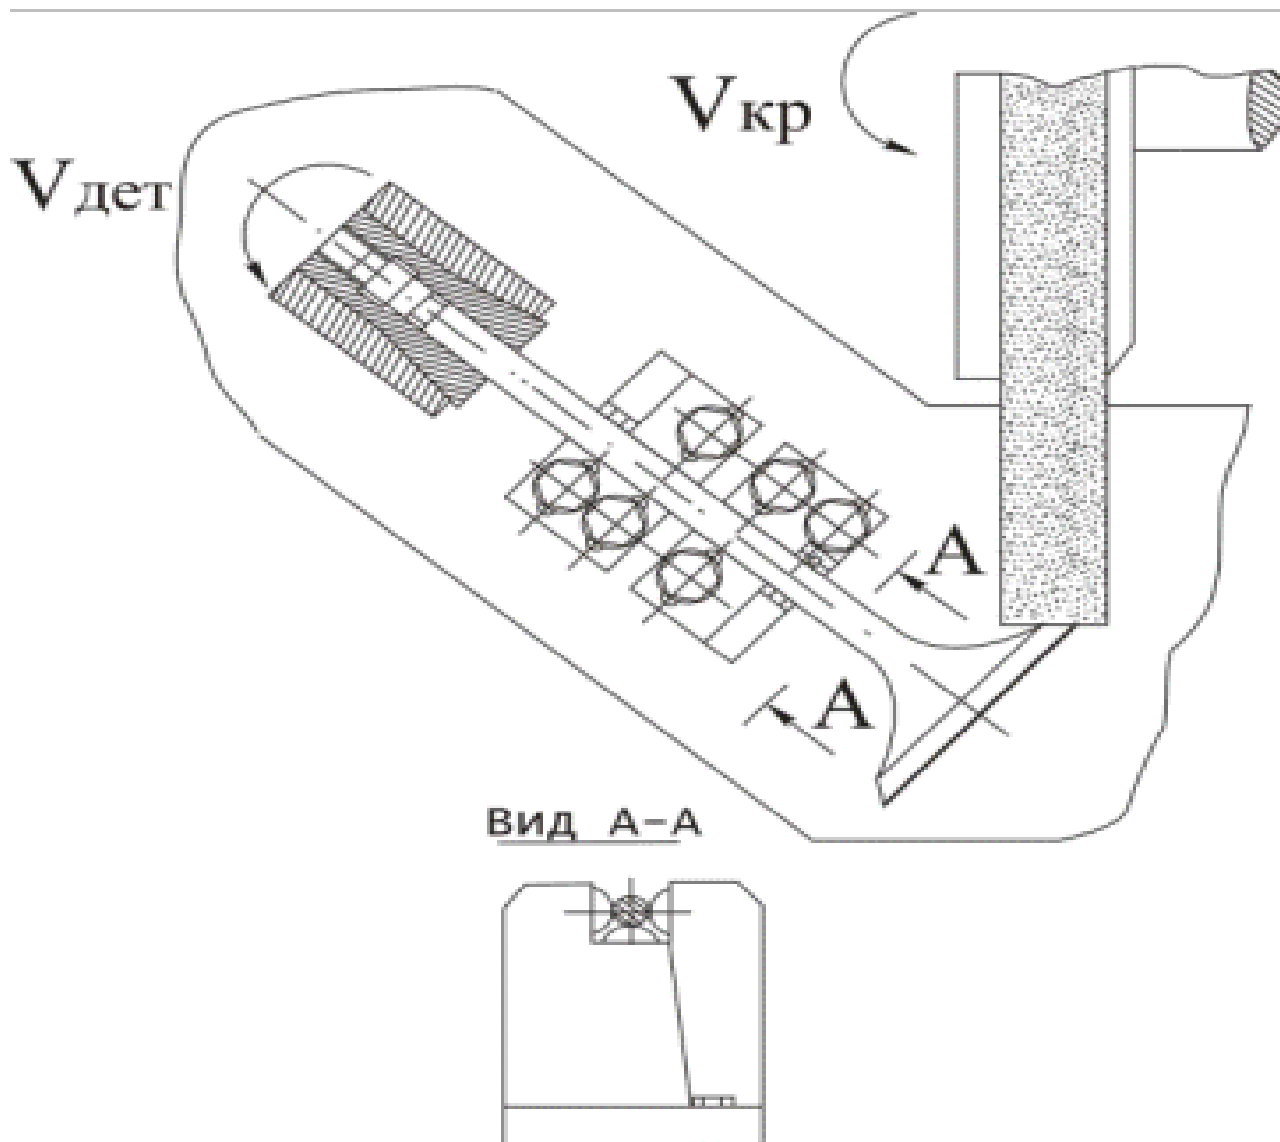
Приспособление для увеличения жесткости крепления клапана в приводе вращения станка.
